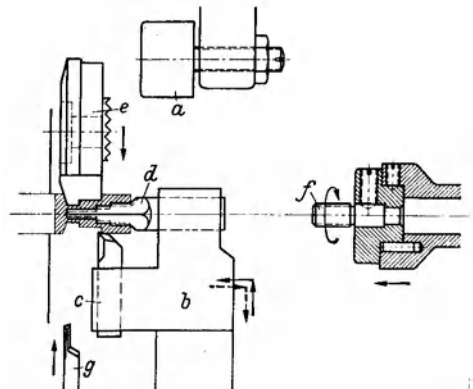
Bearbeitung einer Verschraubung aus Messing.
